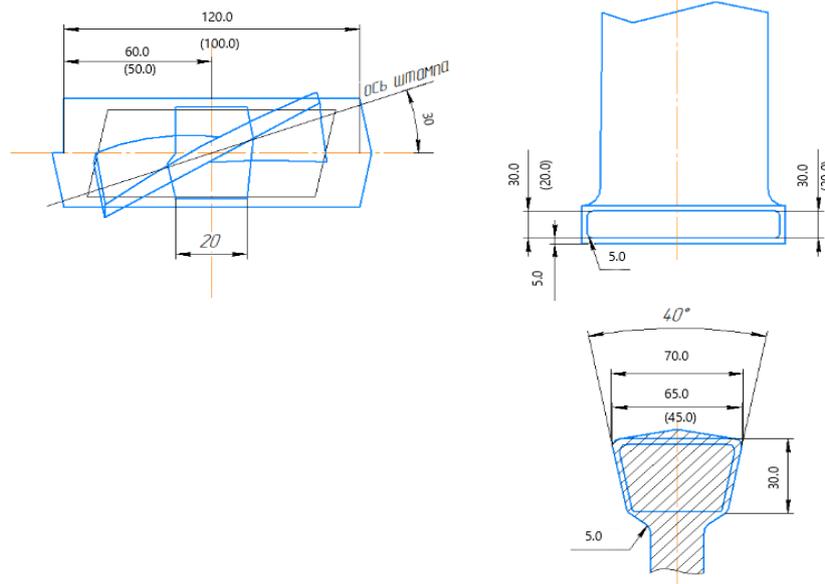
Итоговый чертеж с размерами поковки компрессорной лопатки
